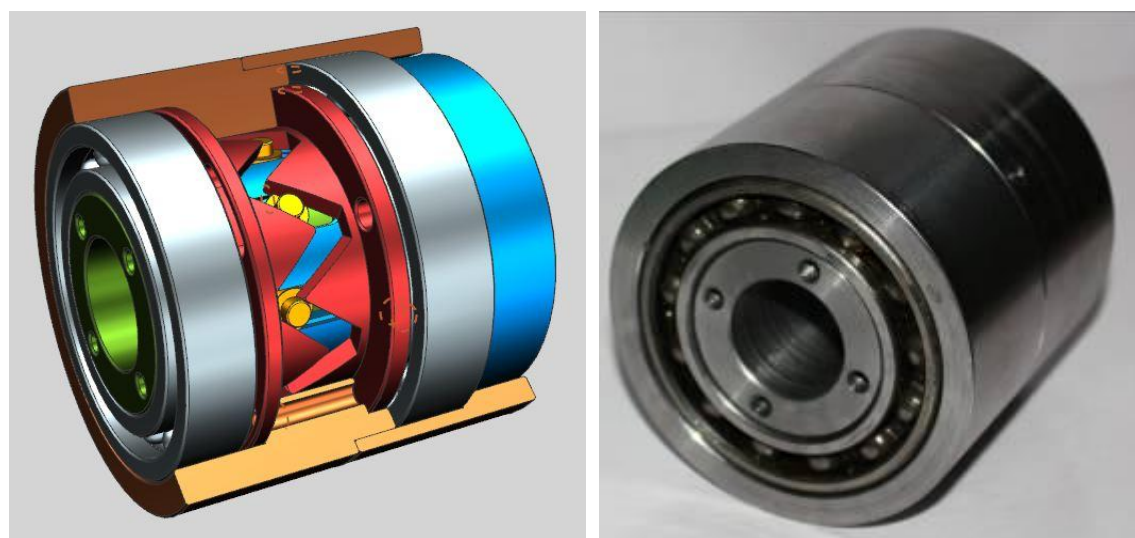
3D-модель и опытный образец редуктора с промежуточными телами качения с «квасивинтовой» формой беговых дорожек
